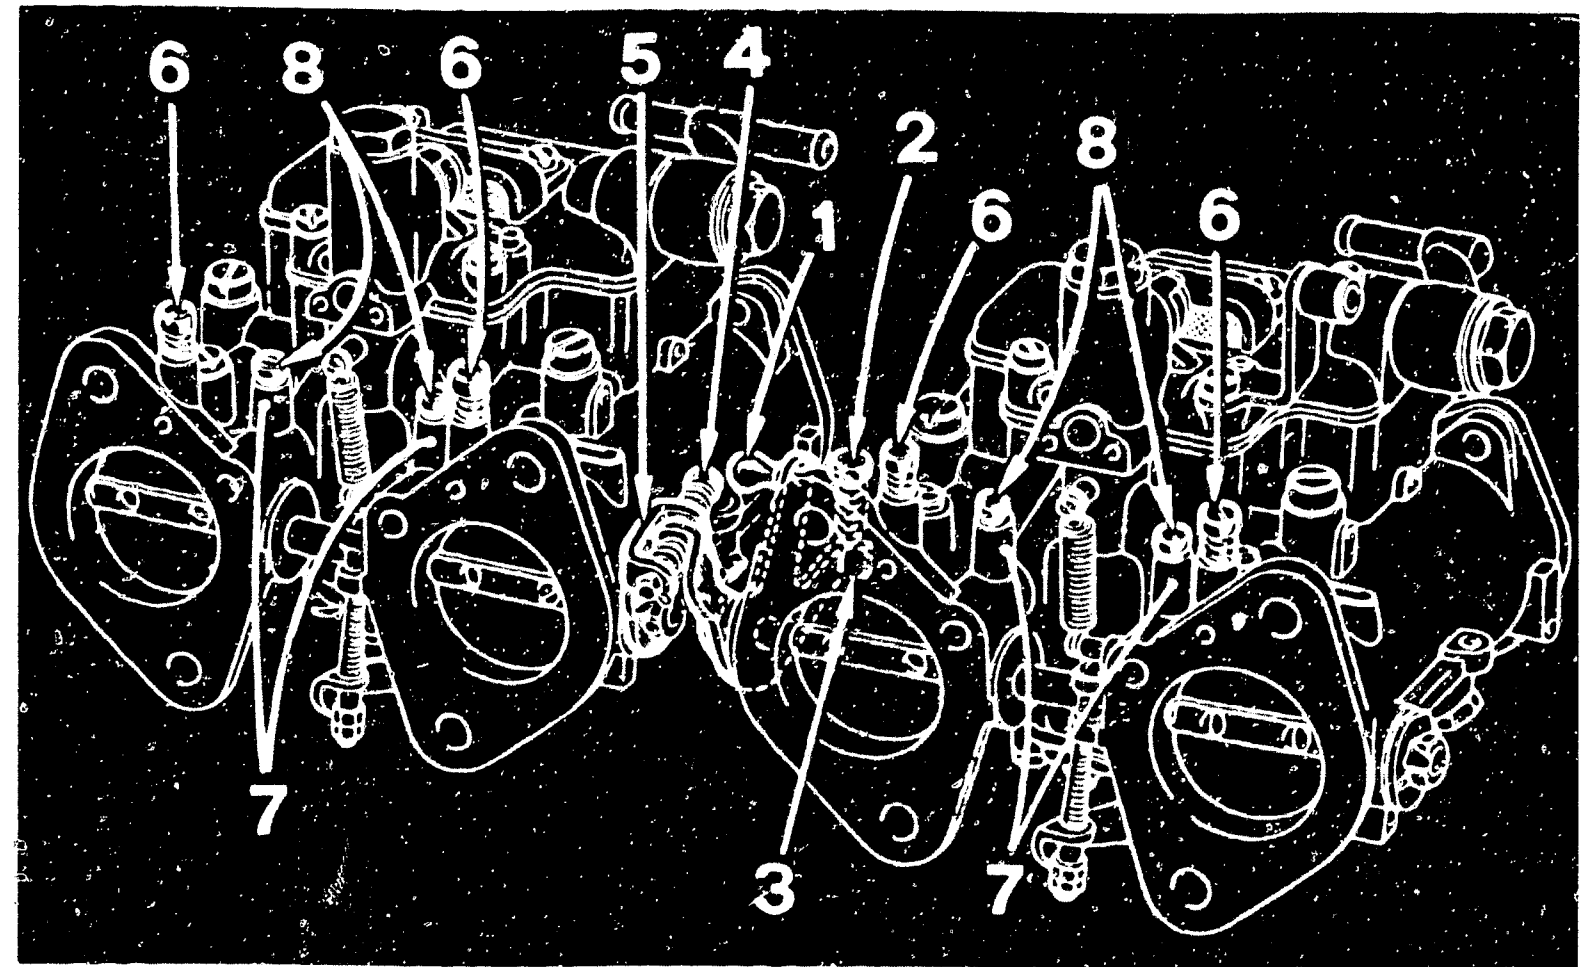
Die Einstellvorrichtung an der Dellorto-Doppelvergaseranlage. 1 Gashebel – 2 Drosselklappenanschlagschraube – 3 Anschlag – 4 Synchronisierschraube für zweiten Vergaser – 5 Drosselhebel – 6 Leerlaufgemischregulierschraube – 7 Luftkompensationsschraube – 8 Verschlusszapfen der Luftkompensationsschraube.
